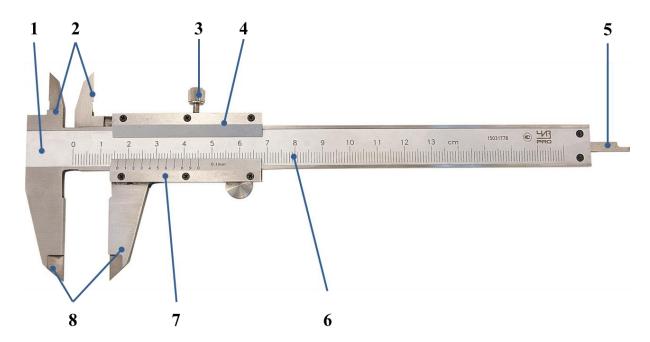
Устройство штангенциркуля типа ШЦ-1:
